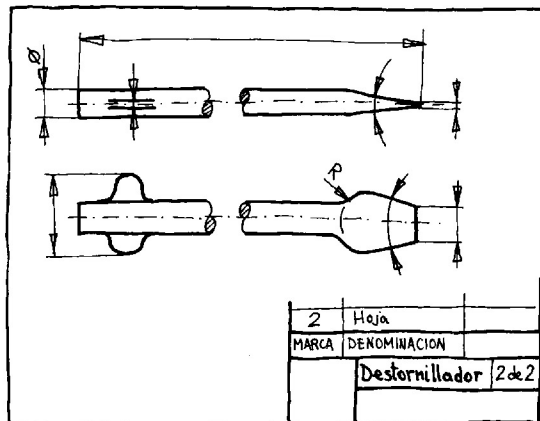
Dibujo de detalle de la hoja del destornillador (elemento a unir)
